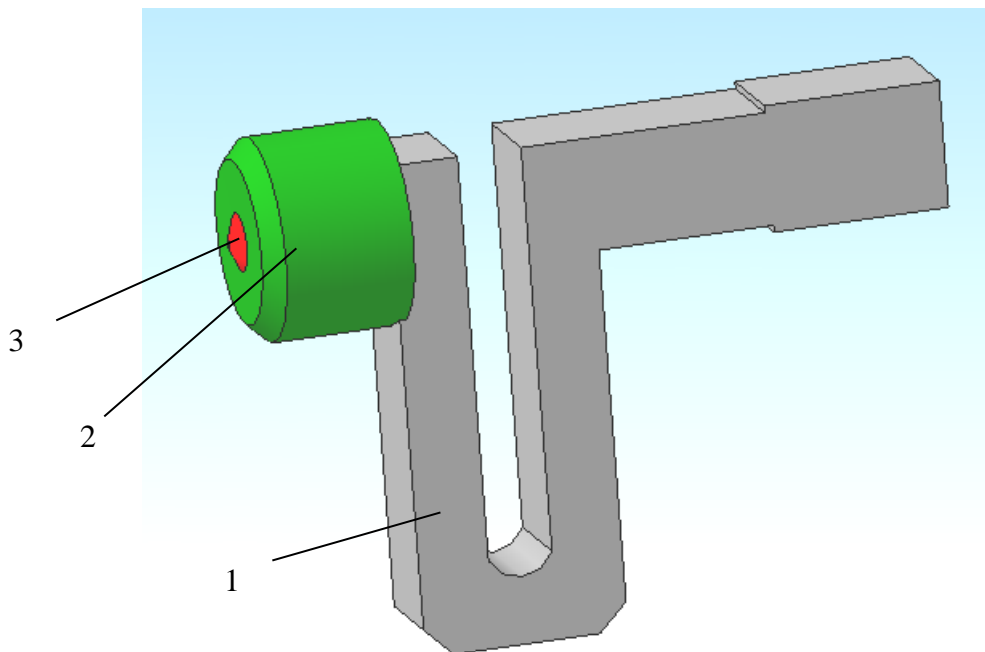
Трьохмірне зображення спеціального інструменту для вигладжування поверхонь обертання: 1 – державка, 2 – оправка, 3 - кулька
